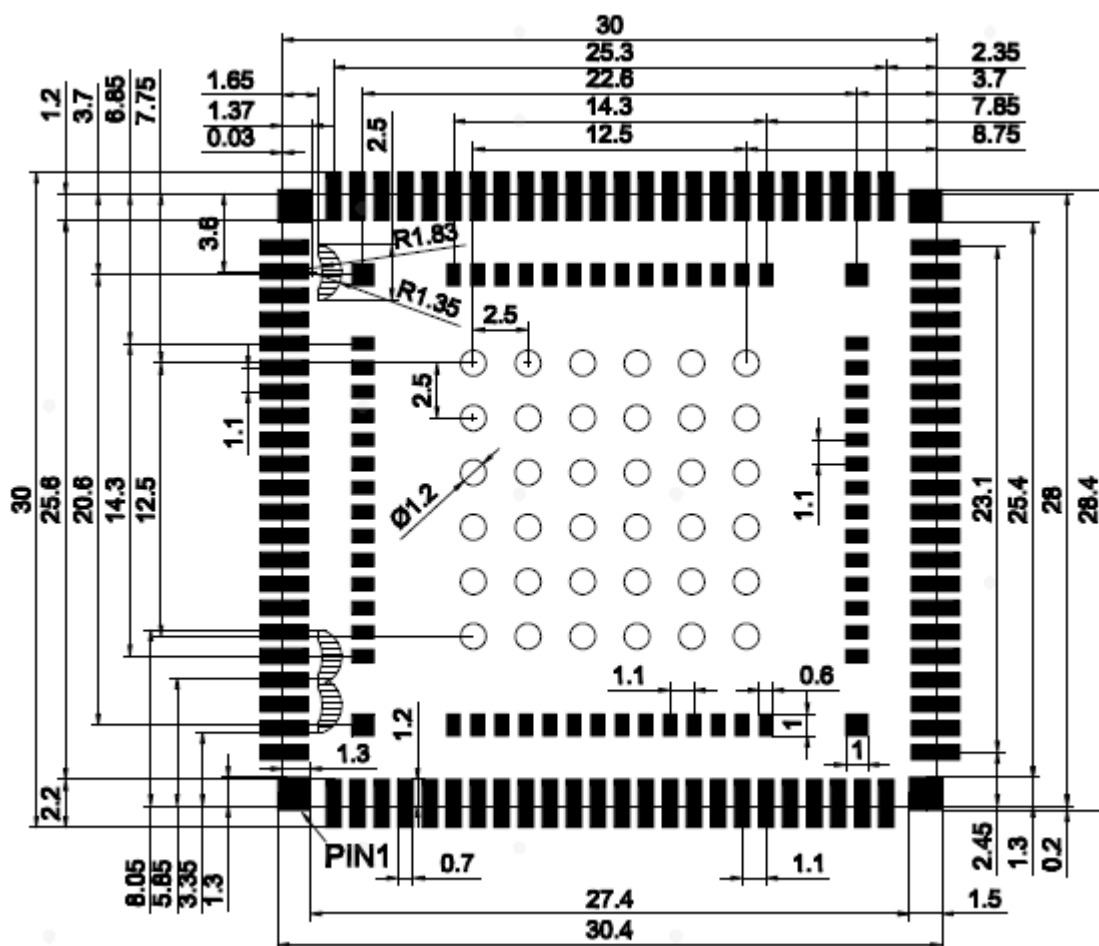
N58 模组应用 PCB 推荐封装俯视图(单位: mm)
